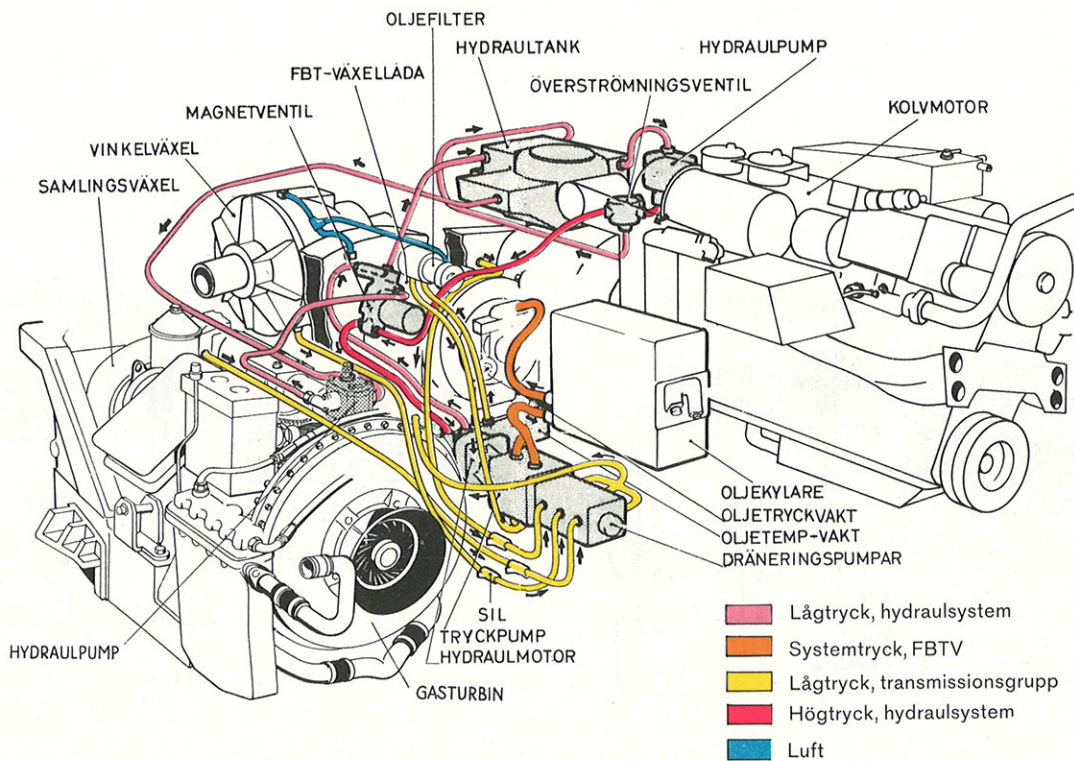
Förloppet i motoraggregatets hydraulsystem under kombinerad drift
